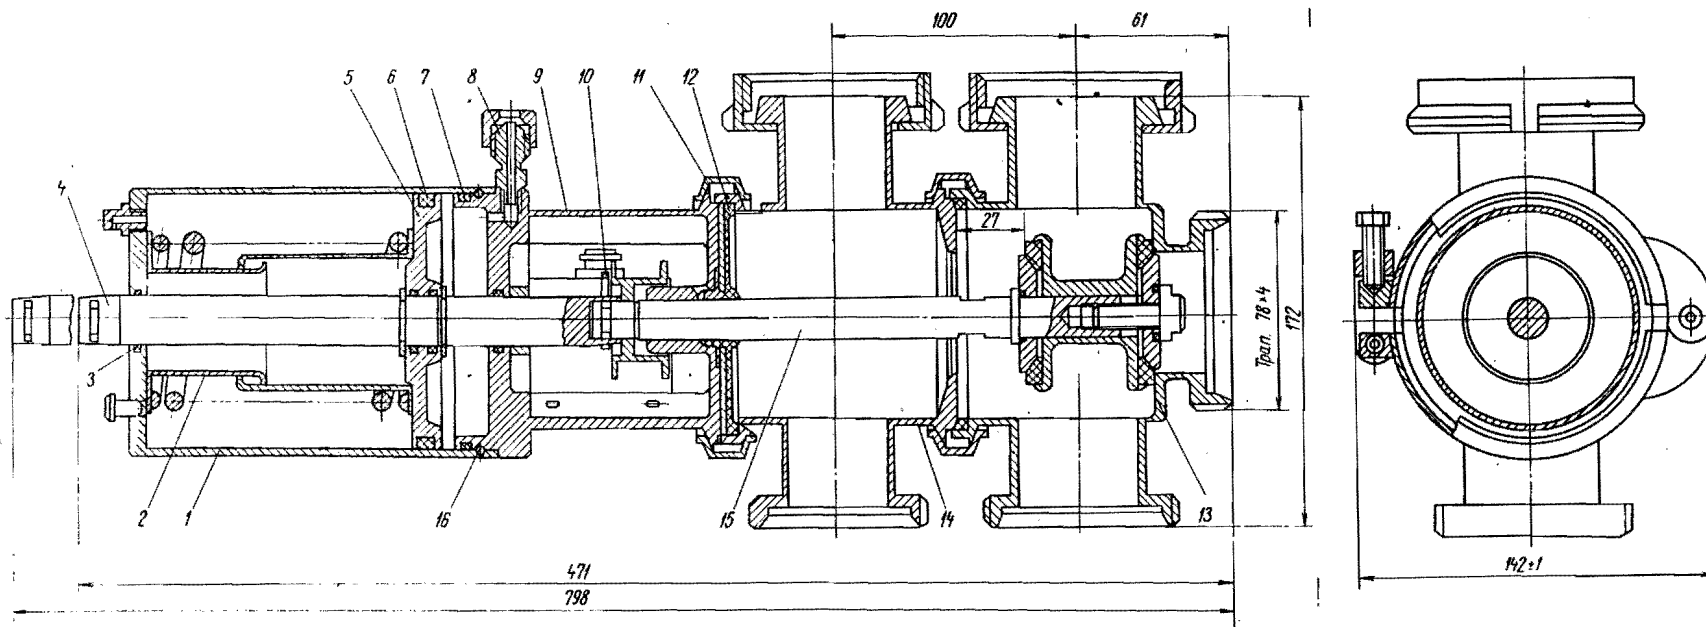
Общий вид клапана марки РЗ-ОПЛ:
